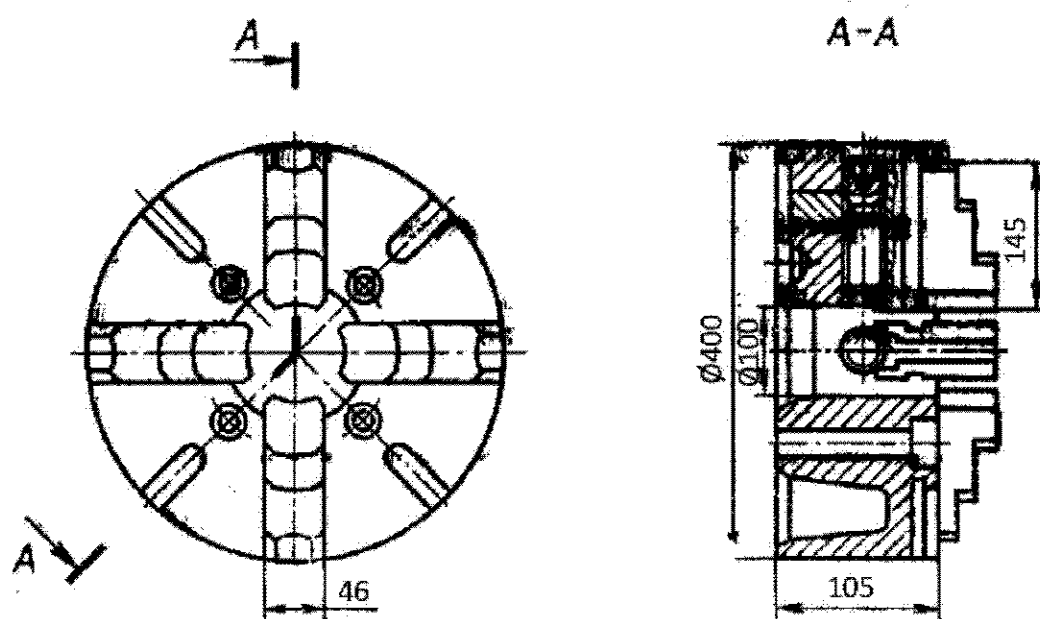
Патрон четырехкулачковый 7103-0049 ГОСТ 3890-82
